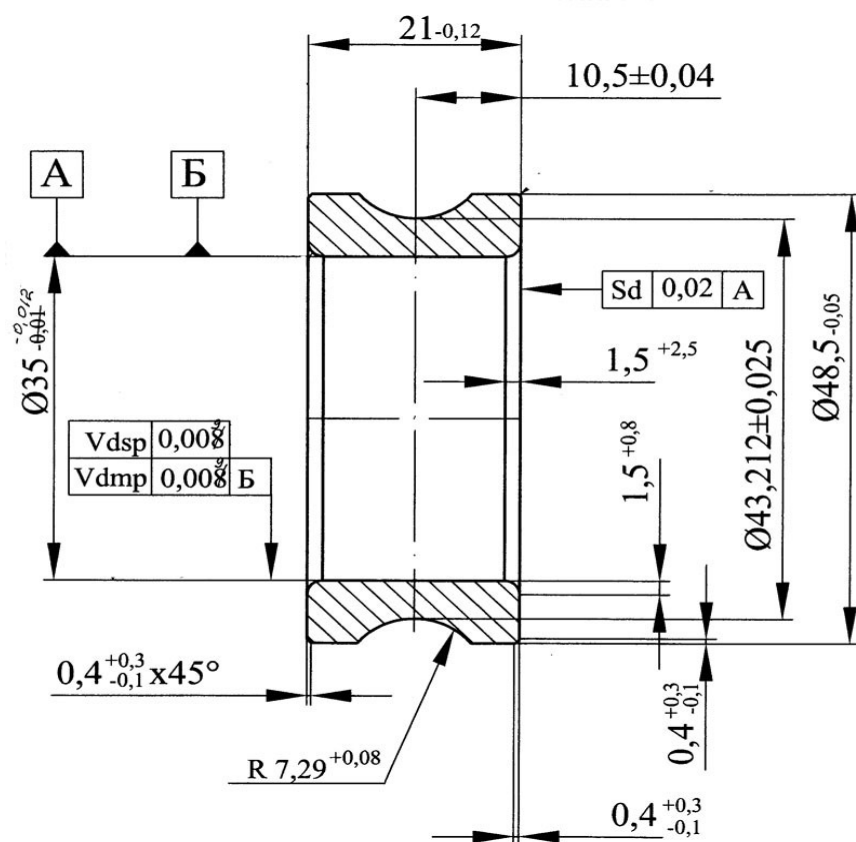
Креслення внутрішнього кільця підшипника 307А
